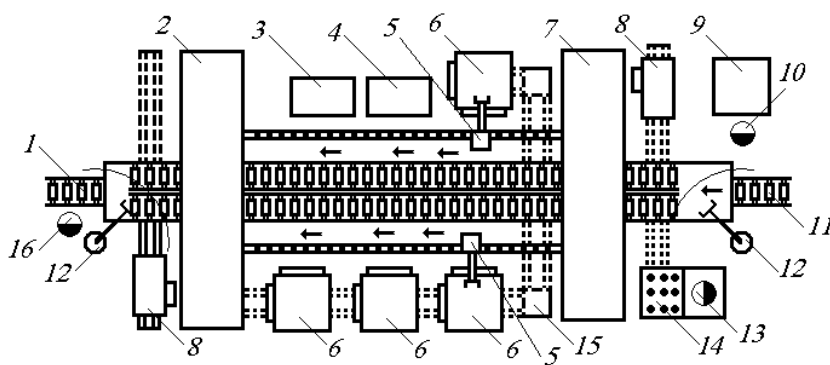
Гибкая автоматическая линия обработки корпусных деталей:
